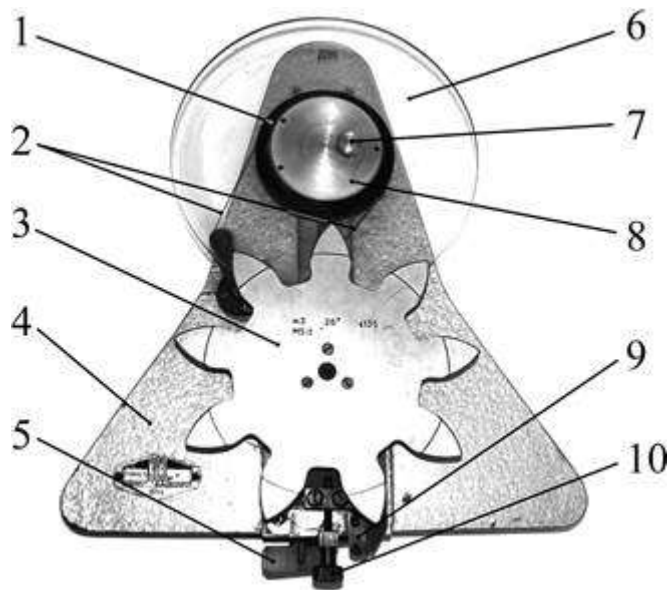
Прибор ТММ–47М для демонстрация принципа изготовления зубчатых колес методом обкатки долбяком
